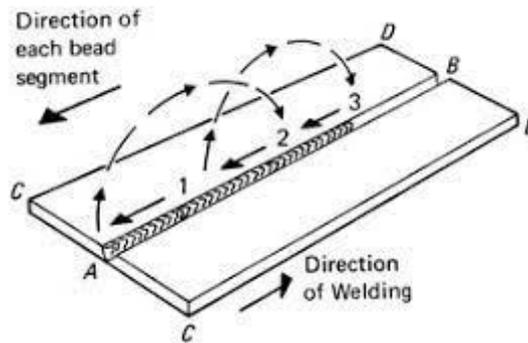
Secuencia del arco en el proceso de soldadura. Fuente: [7]
